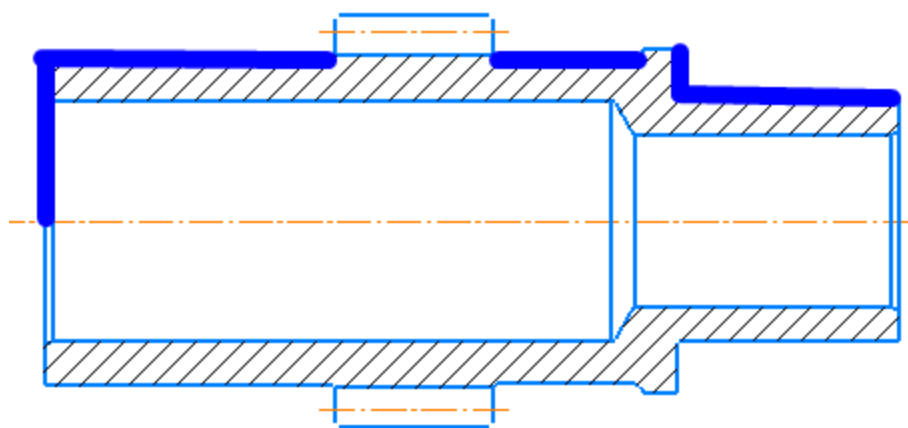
Эскиз детали с отмеченными поверхностями для захвата
